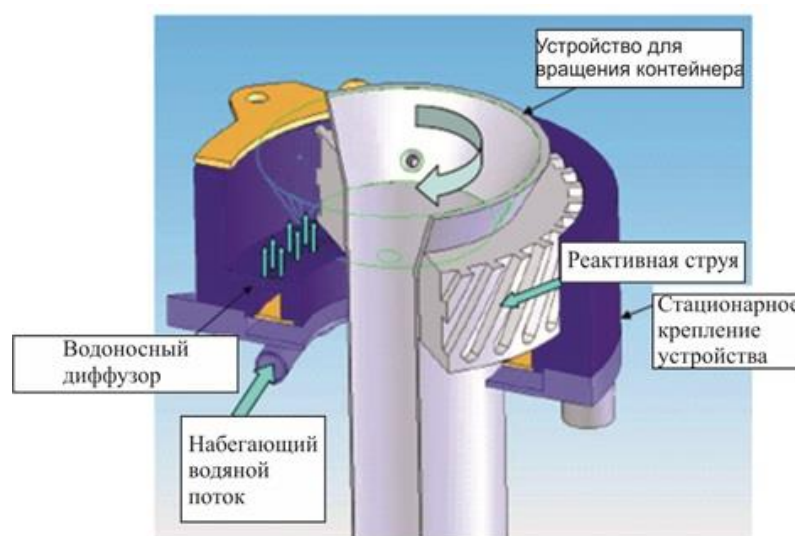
Схема водяного привода установки НТЛ на реакторе OPAL [22]
